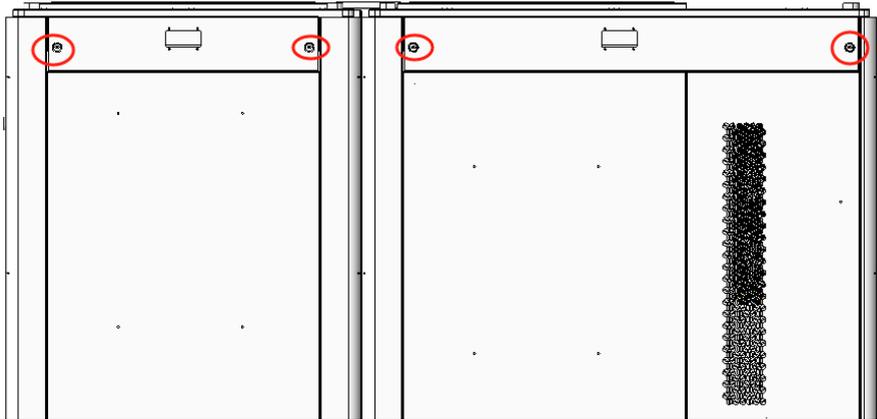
Schematische Darstellung der Demontage der Schrauben der schwenkbaren Abdeckplatte
